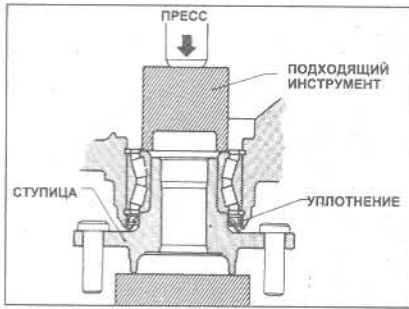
Установка крепежного элемента на ступицу и подшипники (Глава 4)
